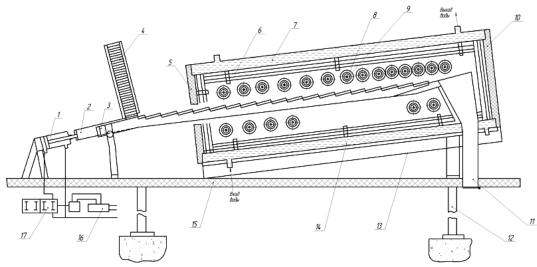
Механизированная терморадиационная печь для нагрева листовых заготовок: 1 — пневматический цилиндр; 2 — подвижная балка; 3 — неподвижная балка; 4 — магазин для заготовок; 5 — задняя стенка; 6 — пачка листов из жароупорной стали; 7 — верхняя часть кожуха печи; 8 — кварцевая трубка; 9 — галогенная кварцевая лампа КГ-220-1000-5; 10 — передняя стенка; 11 — клапан для выдачи заготовок; 12 — ножки печи; 13 — основание печи; 14 — нижняя часть кожуха; 15 — монтажная плита; 16 — реле времени; 17 — электропневматический клапан.
